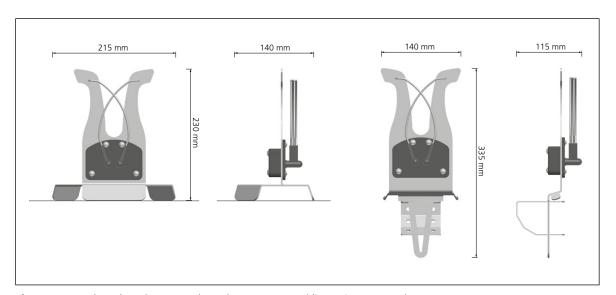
Fred-E 1 | Fred-E 1T vue latérale et vue avant (dimensions en mm)
